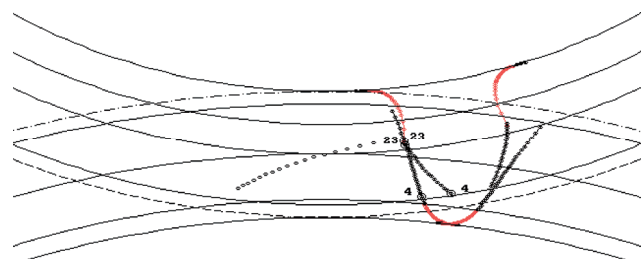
Зацепление профилей боковых поверхностей зубьев зубчатых колес с  $m = 5$ ,  $z_1 = 20$  и  $z_2 = 30$ , образованных инструментальными рейками 1 и 2 с выпуклым и вогнутым профилями боковых поверхностей зубьев
